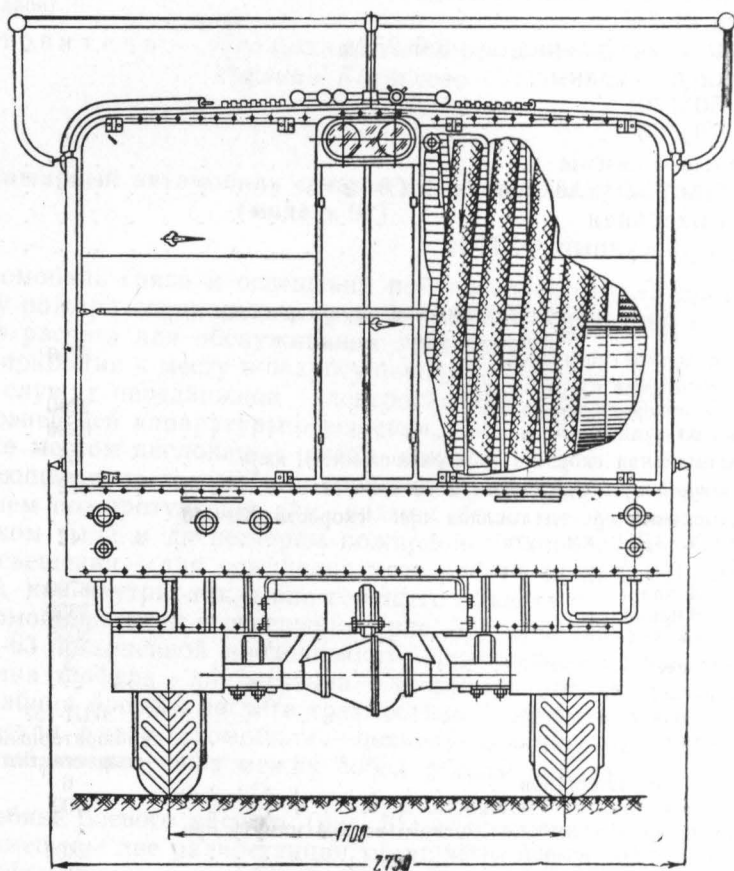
Пожарный рукавный автомобиль АРП-2,2(157): Вид сзади
